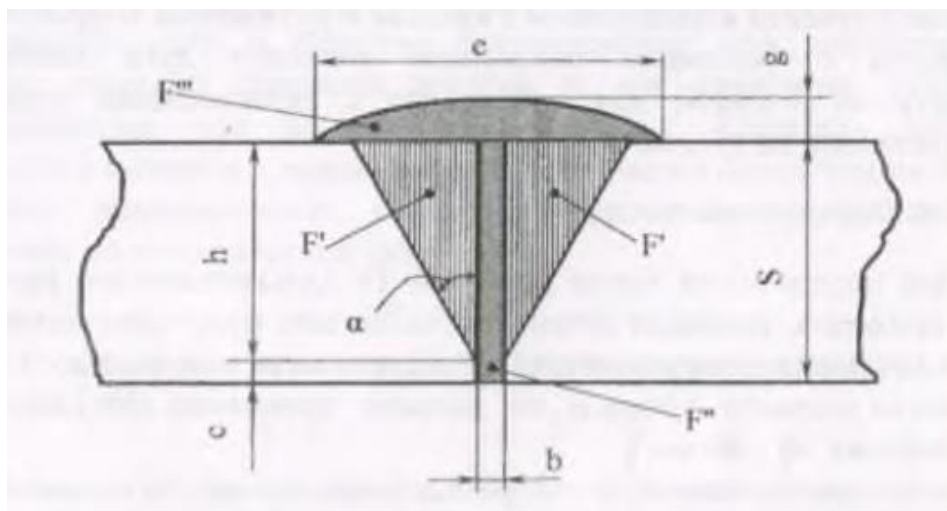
Сечение сварного стыка для нахождения площади сечения наплавленного металла.
